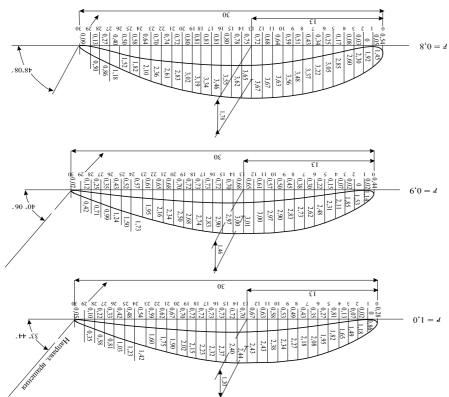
Профили лопатки рабочего колеса ступени K-70-17
